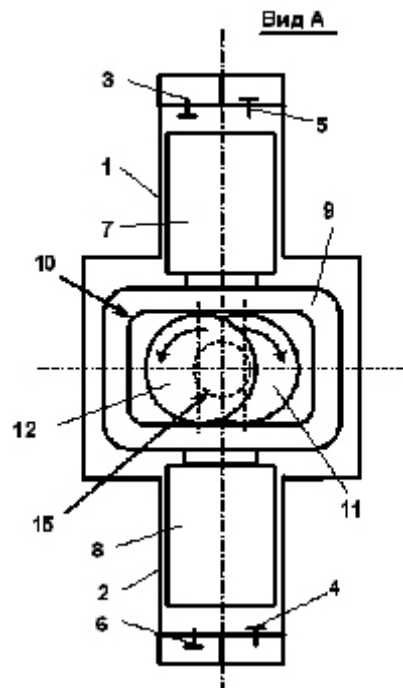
Схема поперечного сечения конструкции оппозитного компрессора с совмещенными электродвигателями (положение блока поршней «вверху»)
